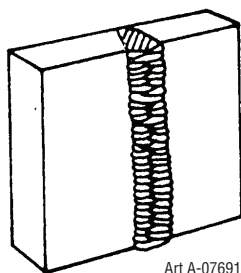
Position verticale, soudure bout à bout
